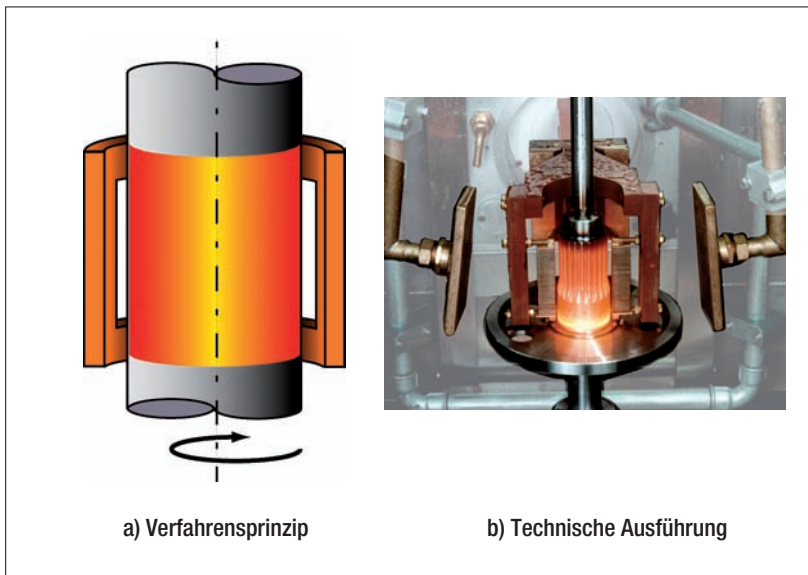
Gesamtflächen-Härtung – Beispiel für Innenfeld-Erwärmen
